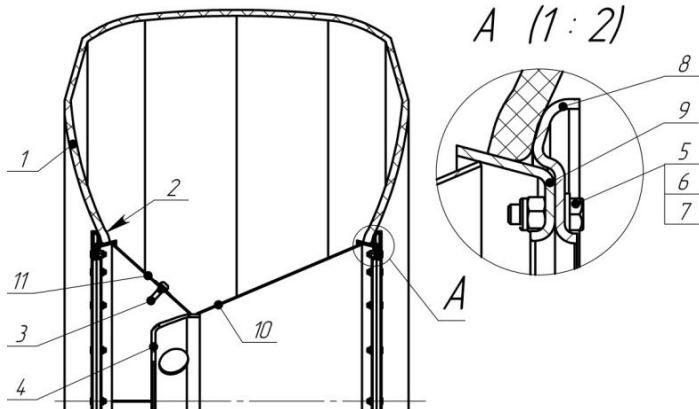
Шина 1600x700-635 ТРЭКОЛ с колесом в сборе
